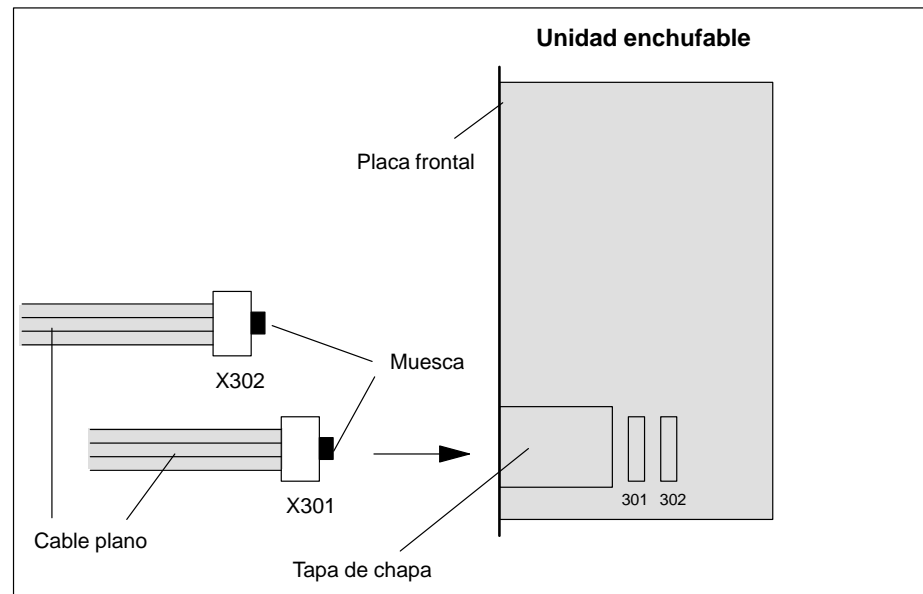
Montaje de los cables planos de la ampliación de eje
